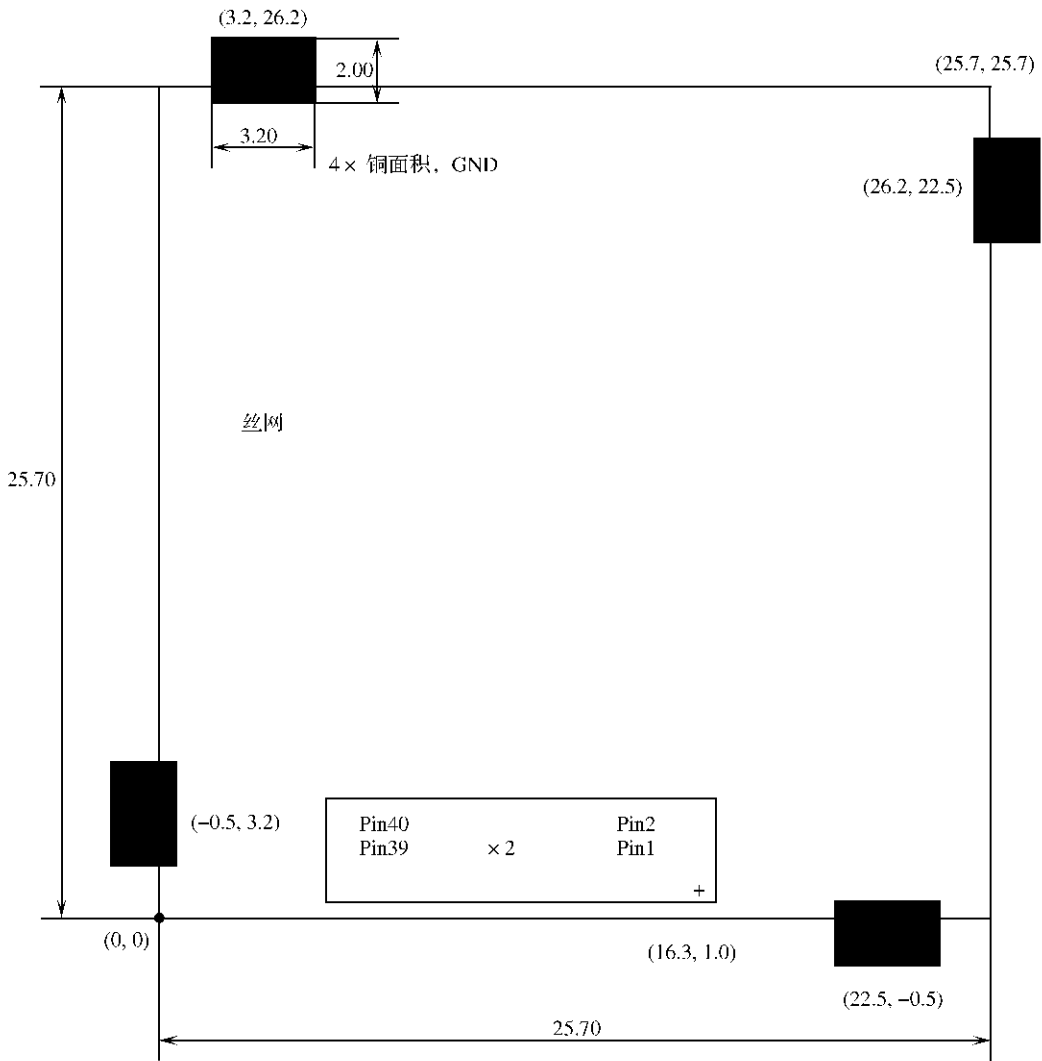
推荐的 ITRAX02 PCB 安装尺寸(单位:mm)
